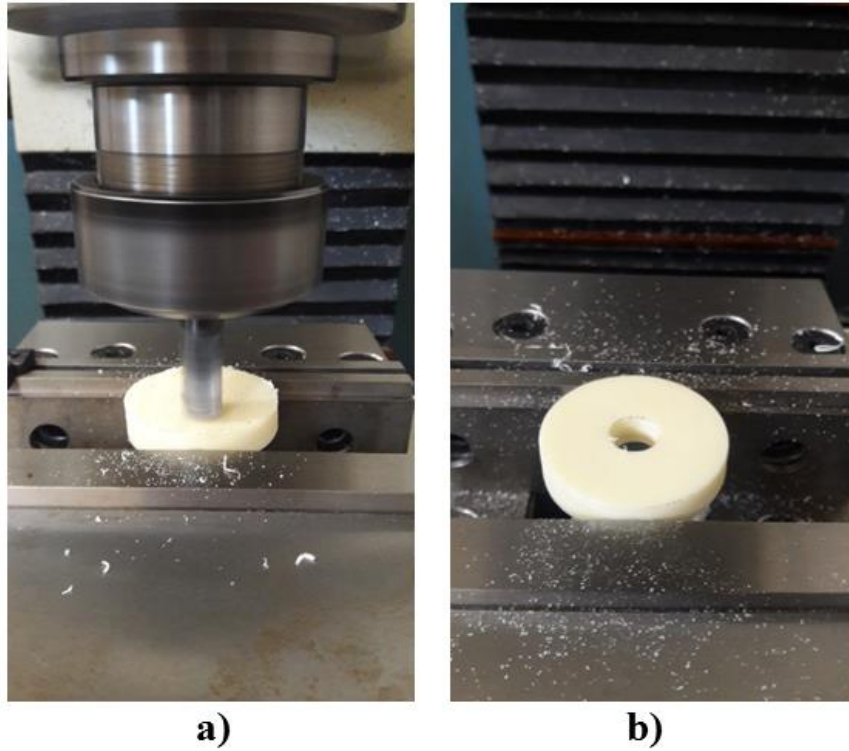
a) Realizando el careado de la pieza en la fresadora CNC, b) Tapa del rodamiento con el espesor de 8.24mm.
